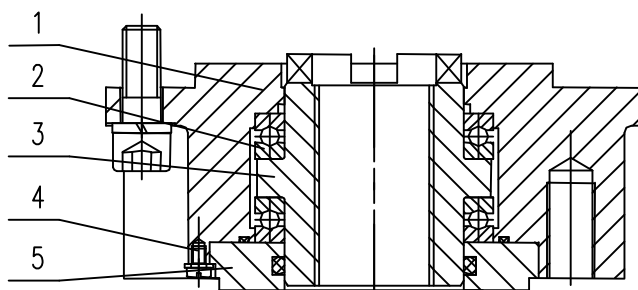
普通推力盘 Fig. 2 Common thrust attachmen
